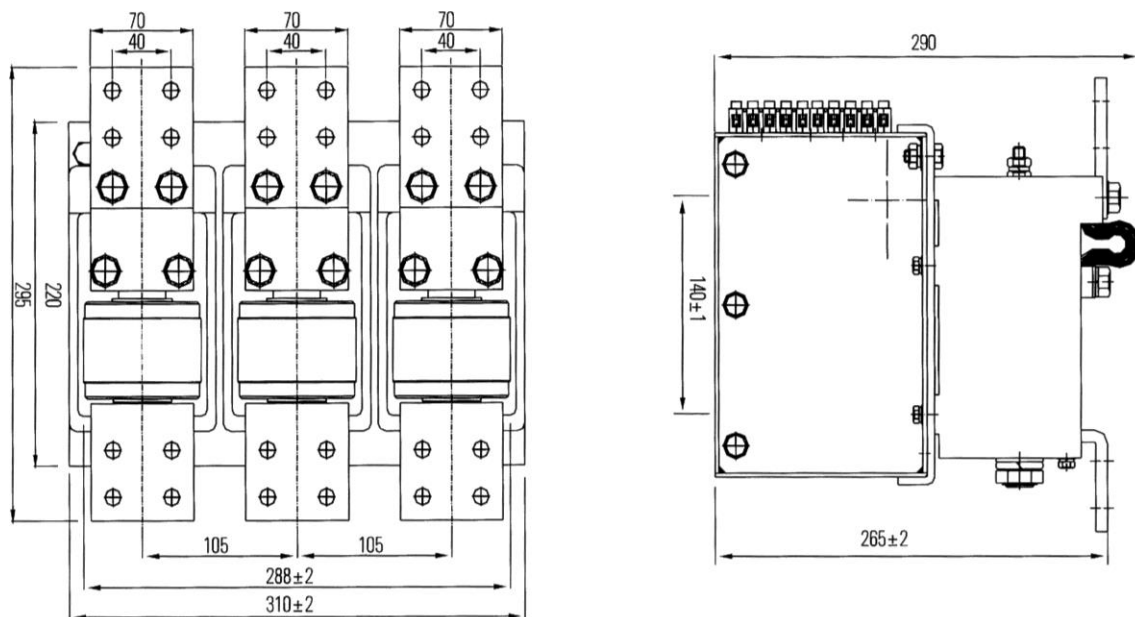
Габаритные размеры КВТ-1,14-1000/1250/1600
